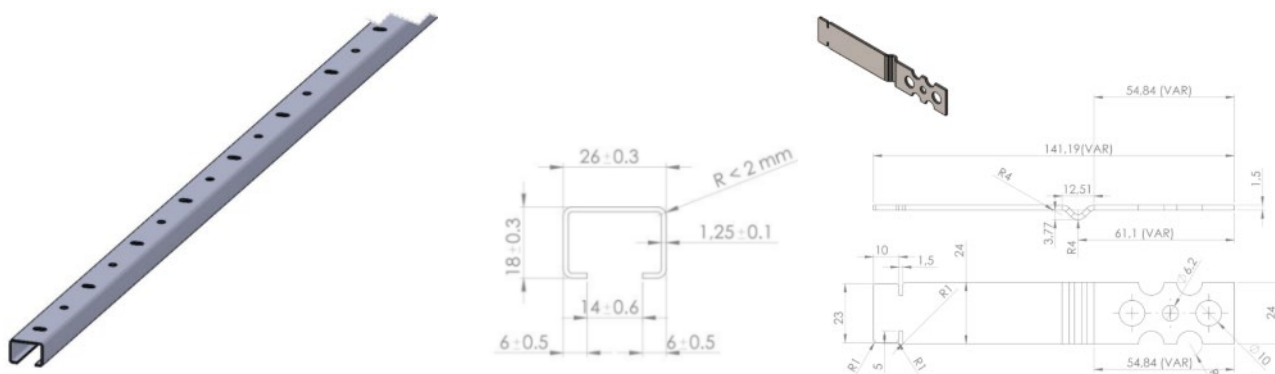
Attaches FIXIBOIS de type CB et rail en C de type B
